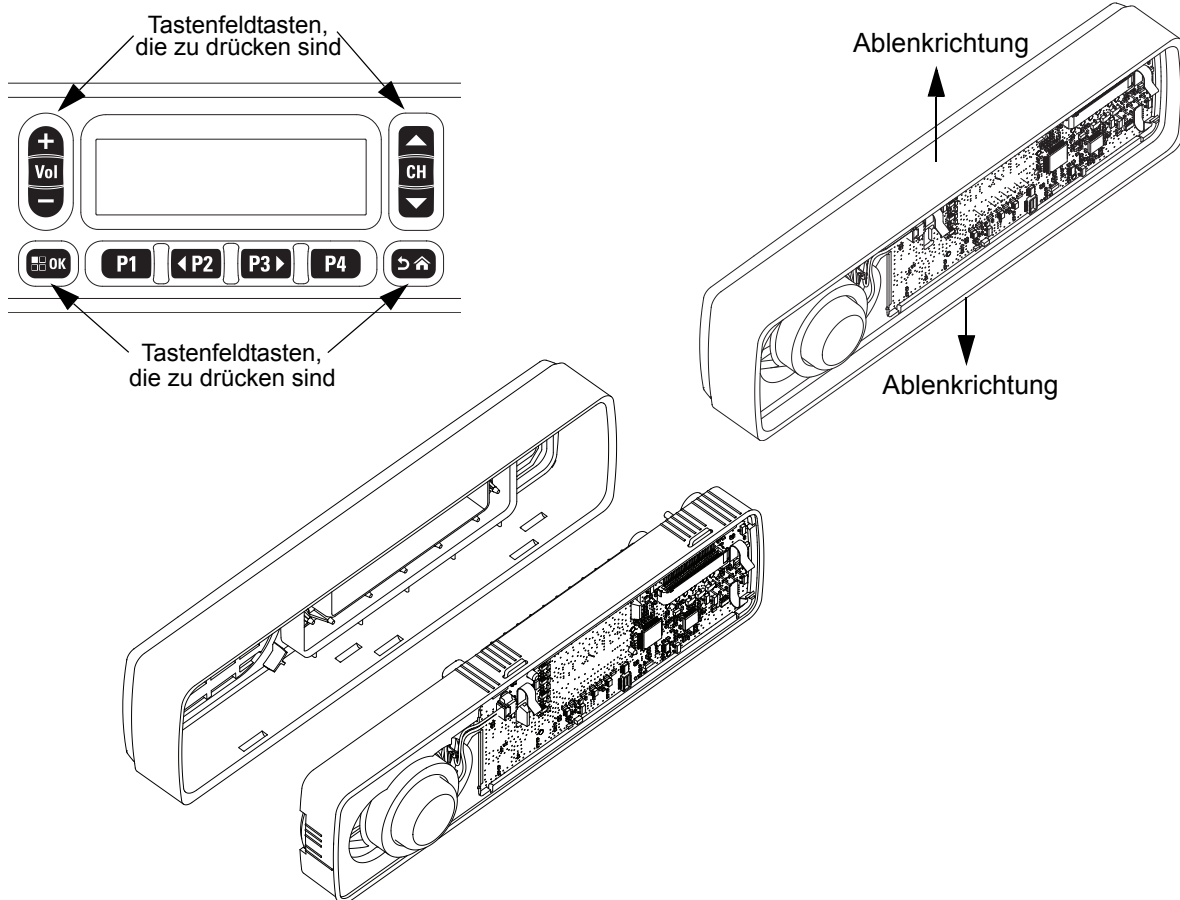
Tastenfeld-Baugruppe entfernen
